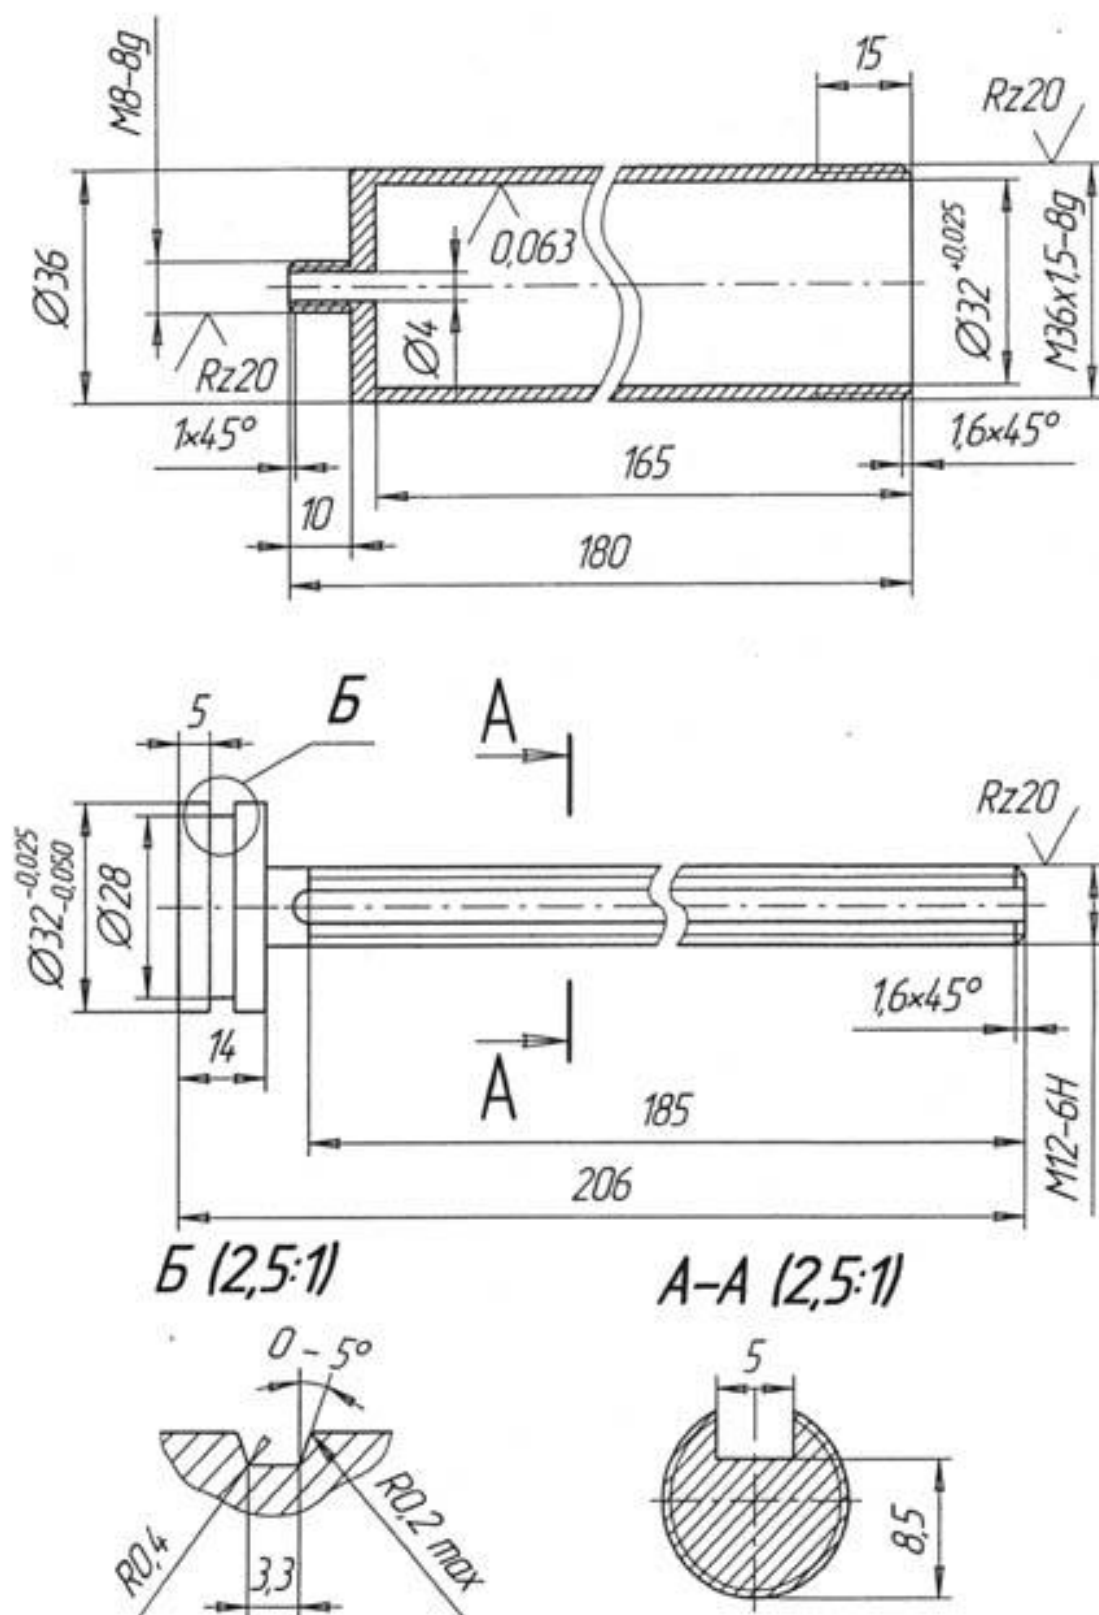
Конструкция деталей цилиндра с изменяемым "мертвым" объемом
